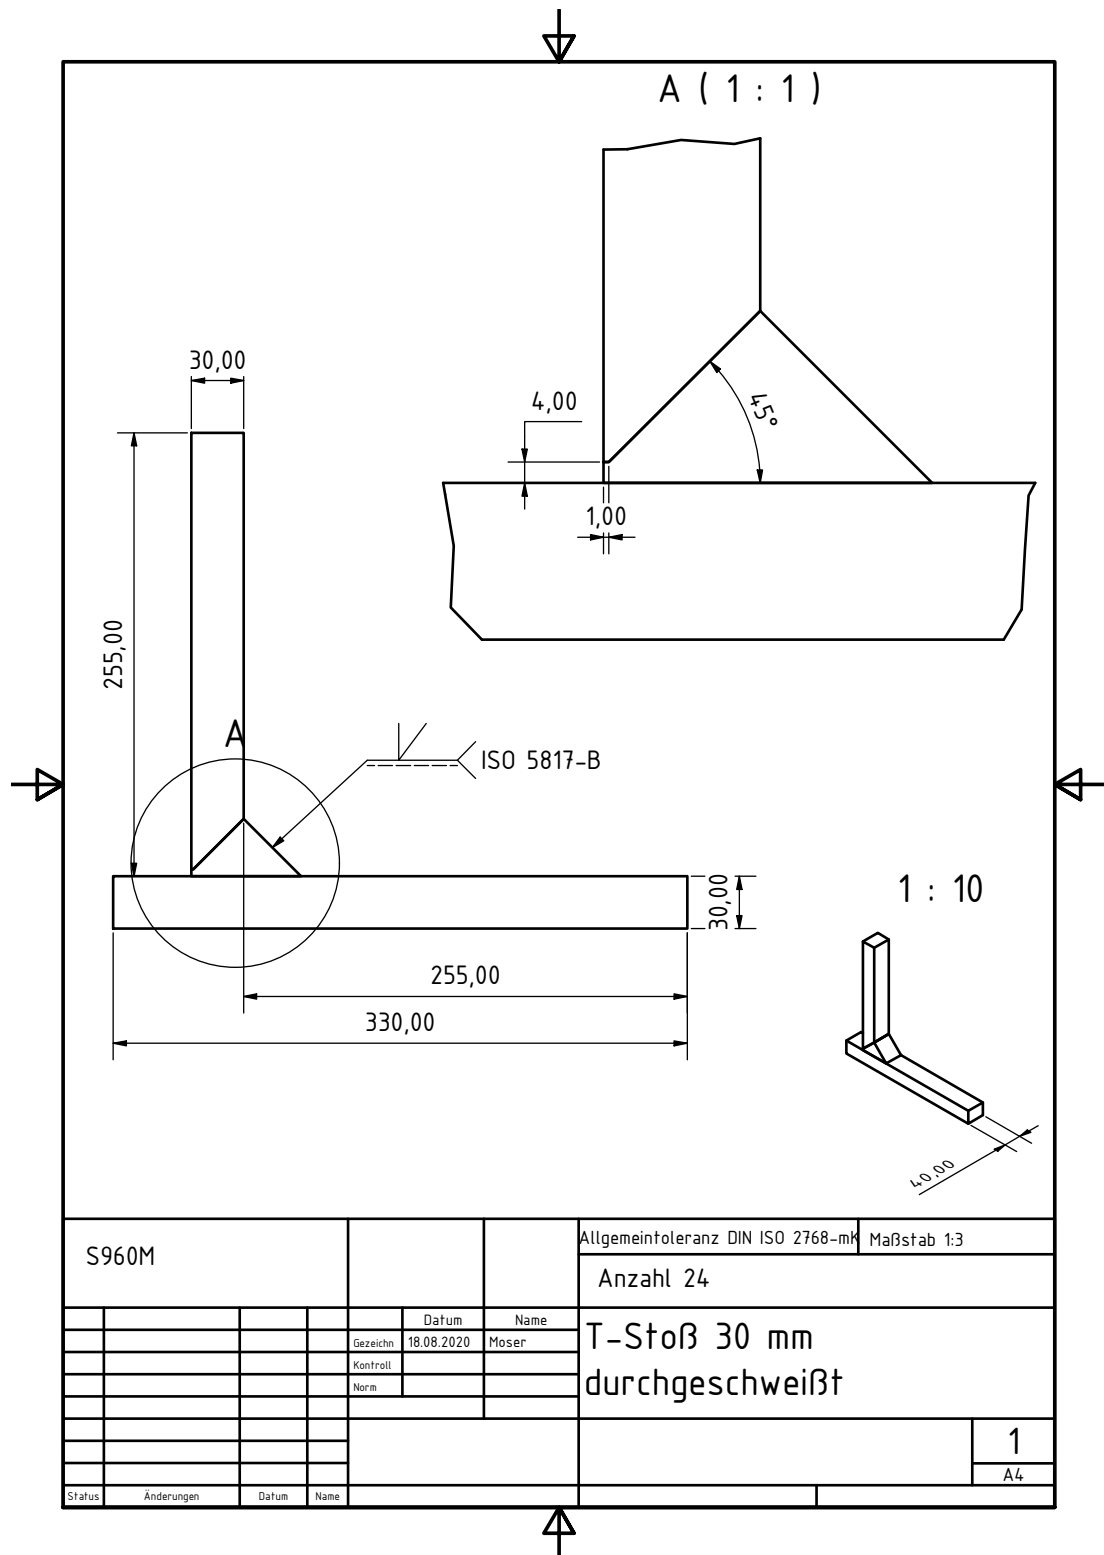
Fertigungszeichnung für die T-Stoß Proben aus S960M.
